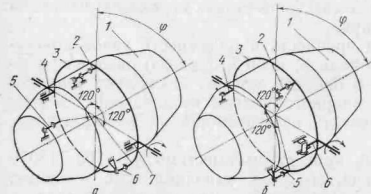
Системы крепления корпуса конвертера в опорном кольце
